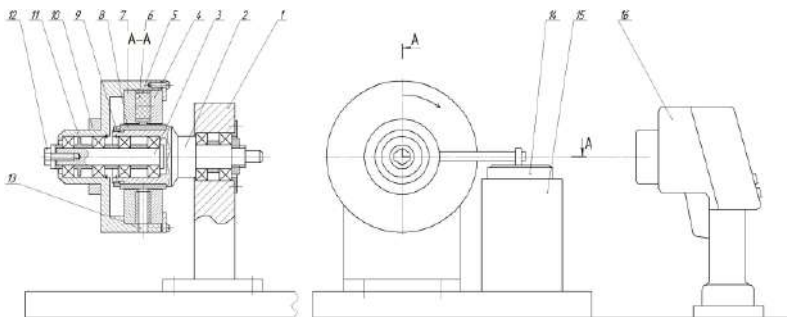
Схема экспериментальной установки: 1 – стойка; 2 – подвижный вал; 3 – неподвижный вал; 4 – съемный полюс; 5 – диск (обойма); 6 – магнит; 7 – съемный полюс; 8 – сменная втулка; 9 – гайка; 10 – хомут; 11 – корпус; 12 – болт; 13 – отверстие для измерения температуры; 14 – весы; 15 – стойка; 16 – тепловизор
